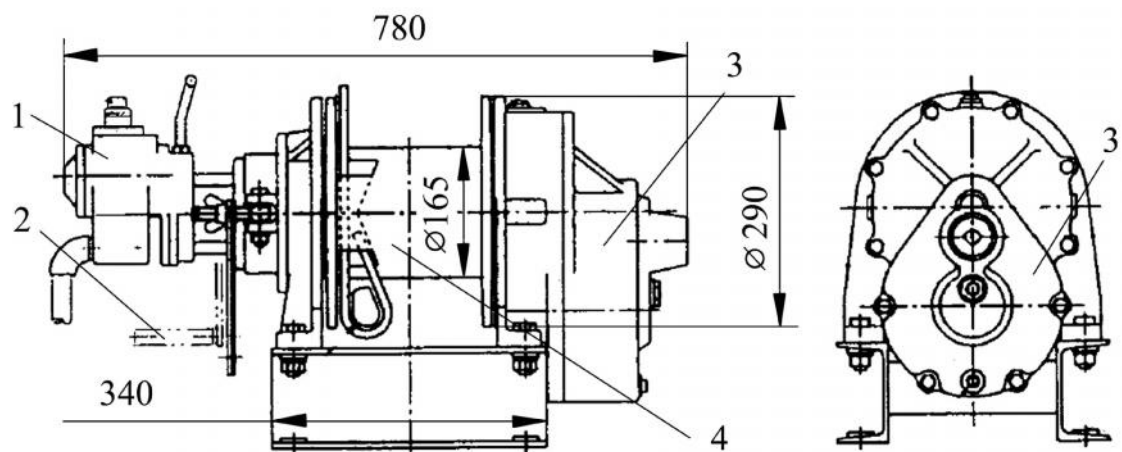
Общий вид грузовой лебедки: 1 – пневмодвигатель;
